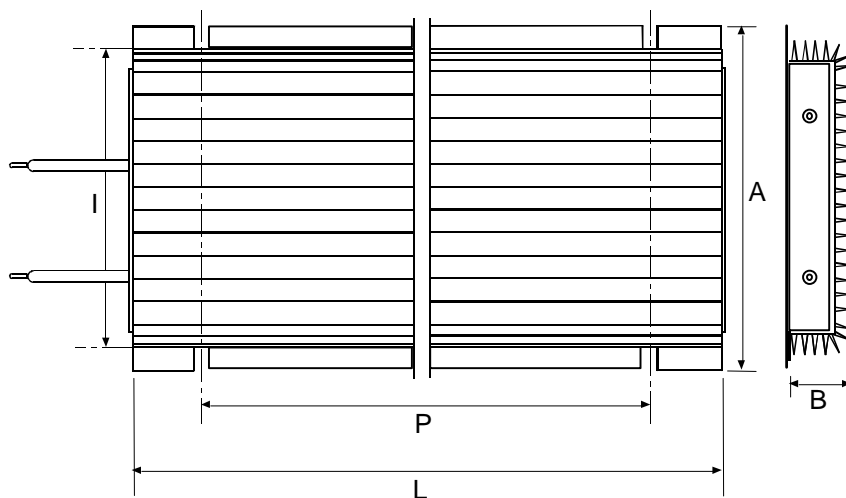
Размеры и параметры тормозного резистора 75 Ом/1300 Вт
